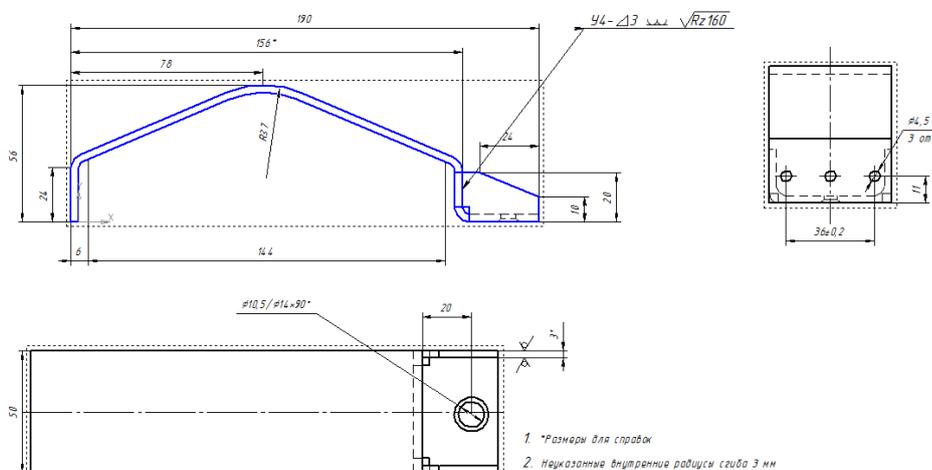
Чертеж скобы, выполненный по 3D-модели
